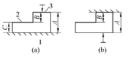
工件的定位夹紧方式 1-大表面 2-加工表面 3-小平面
